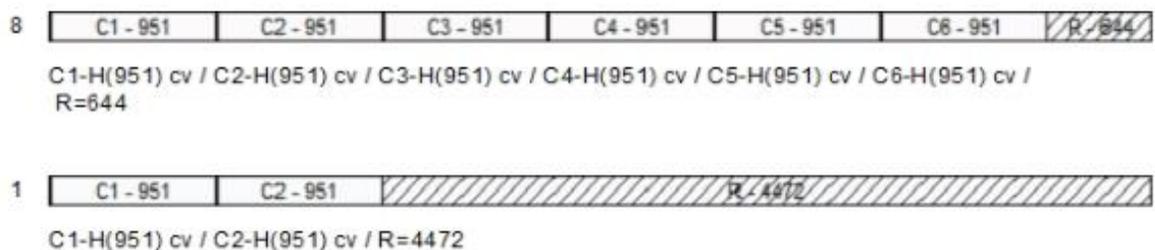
Cortes de barras de travesaño para 50 ventanas con travesaño.
